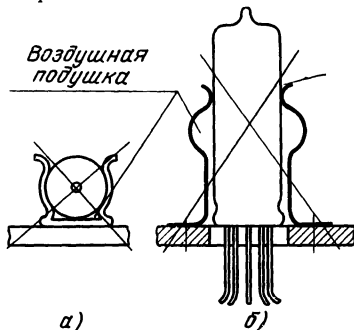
Неудачные конструкции держателей для сверхминиатюрных ламп.
